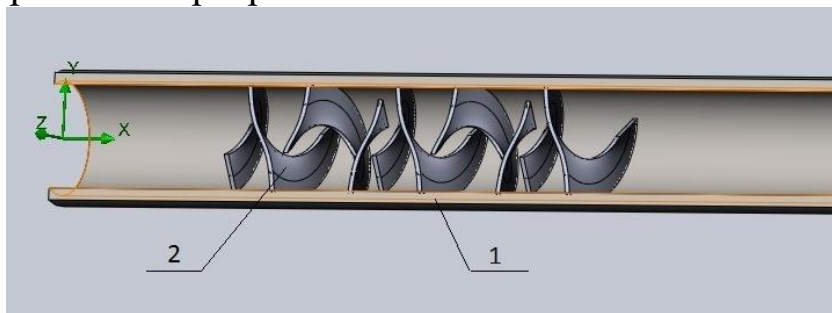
3D-модель конструкції статичного змішувача:
